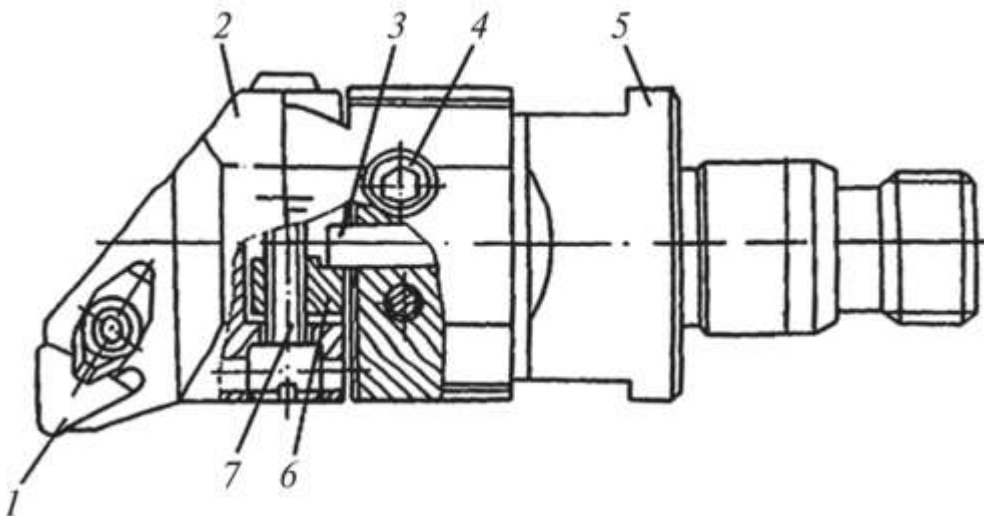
Схема регульованої однолезової розточувальної збірної головки
